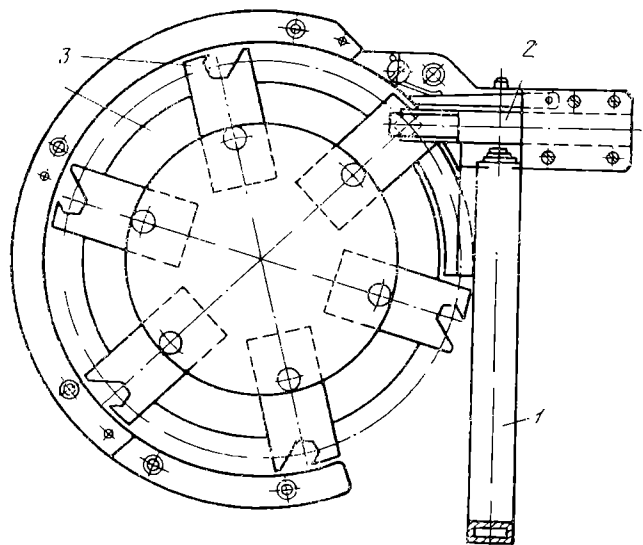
Устройство для подачи заготовок в двухпозиционный штамп
